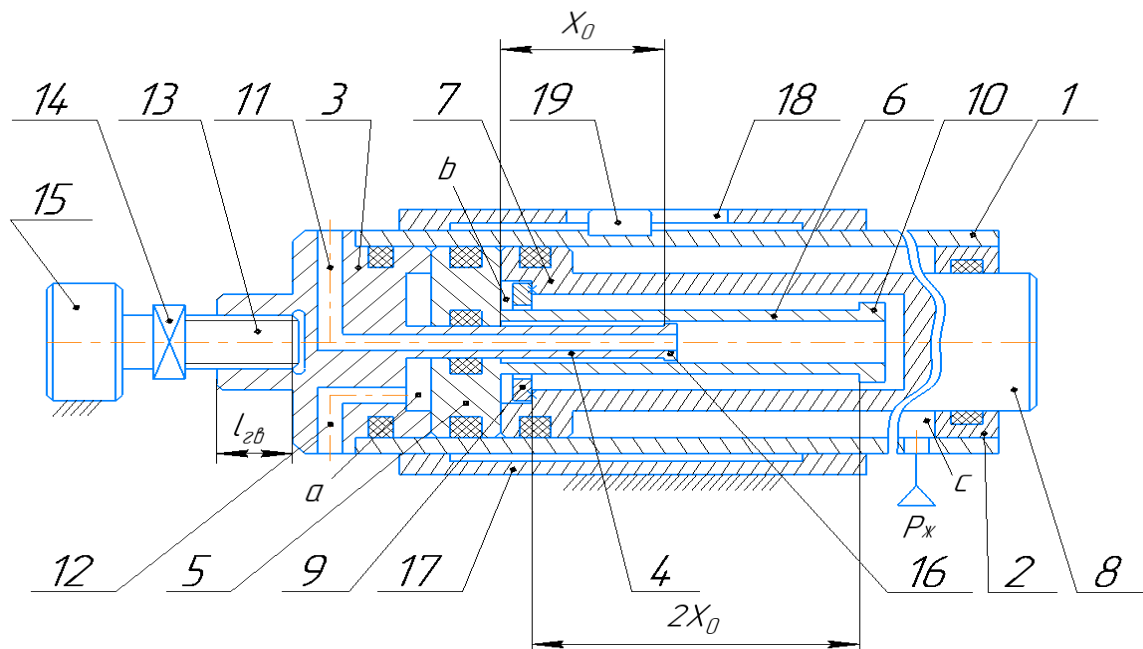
Комбінований електропневматичний багатопозиційний привод руки промислового робота.
